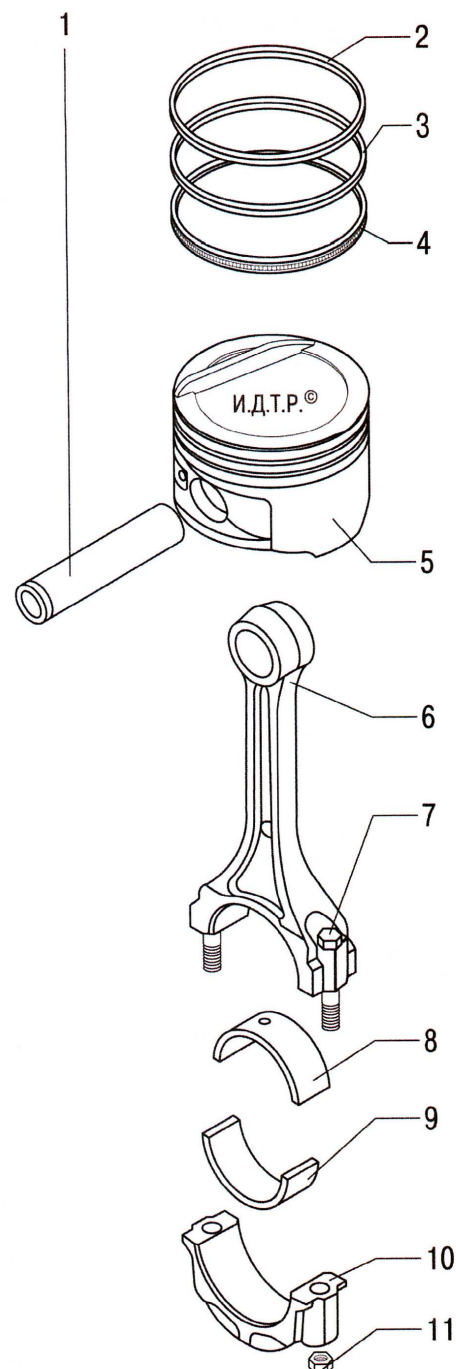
Шатунно-поршневая группа двигателя G4GC: 1 – поршневой палец; 2 – верхнее компрессионное кольцо; 3 – нижнее компрессионное кольцо; 4 – маслосъемное кольцо; 5 – поршень; 6 – шатун; 7 – болт шатуна; 8, 9 – вкладыши шатунного подшипника; 10 – крышка шатуна; 11 – гайка болта шатуна
